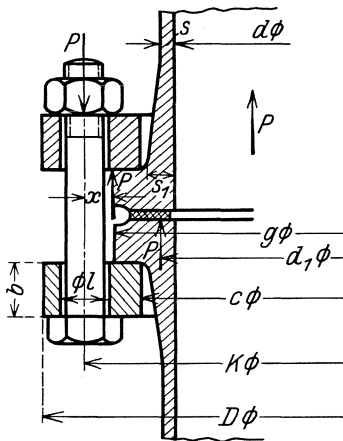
Stahlrohrverbindung durch lose Flansche.
